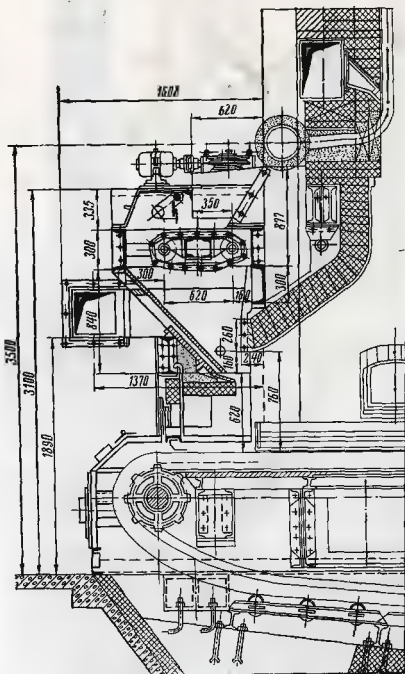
Пневматический забрасыватель «ВТИ-Комега»
